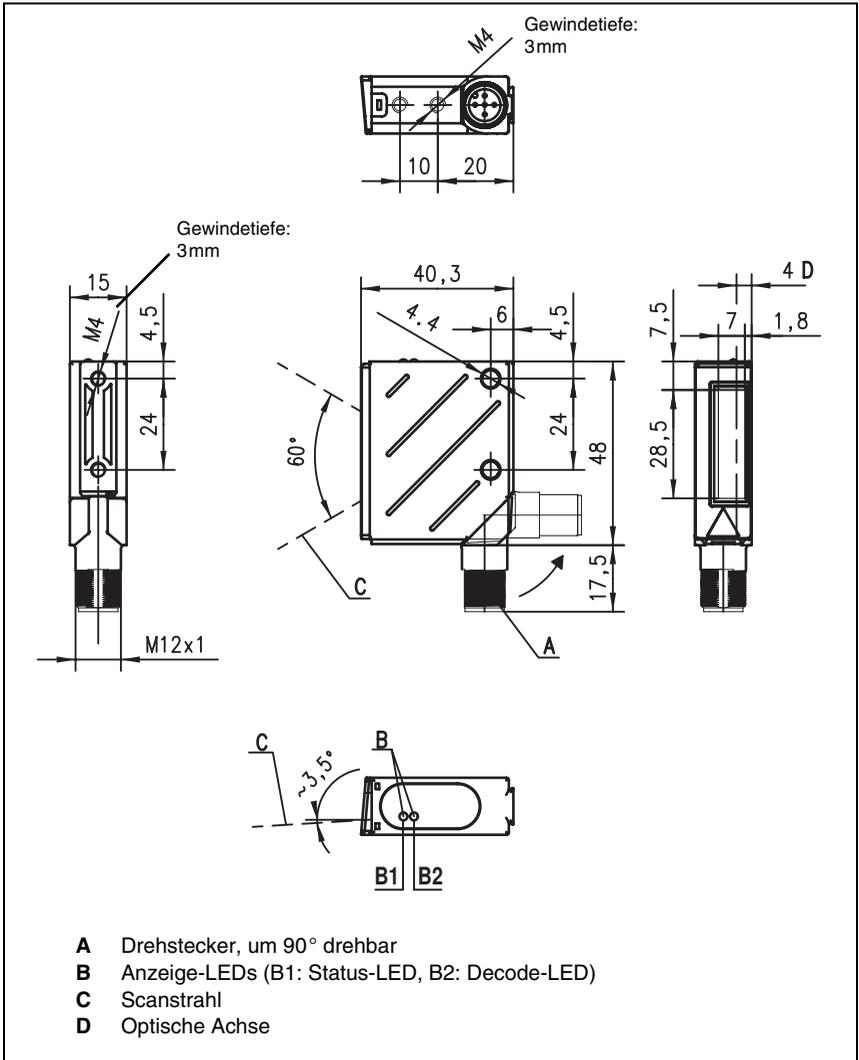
Maßzeichnung BPS 8 SM 102-01
